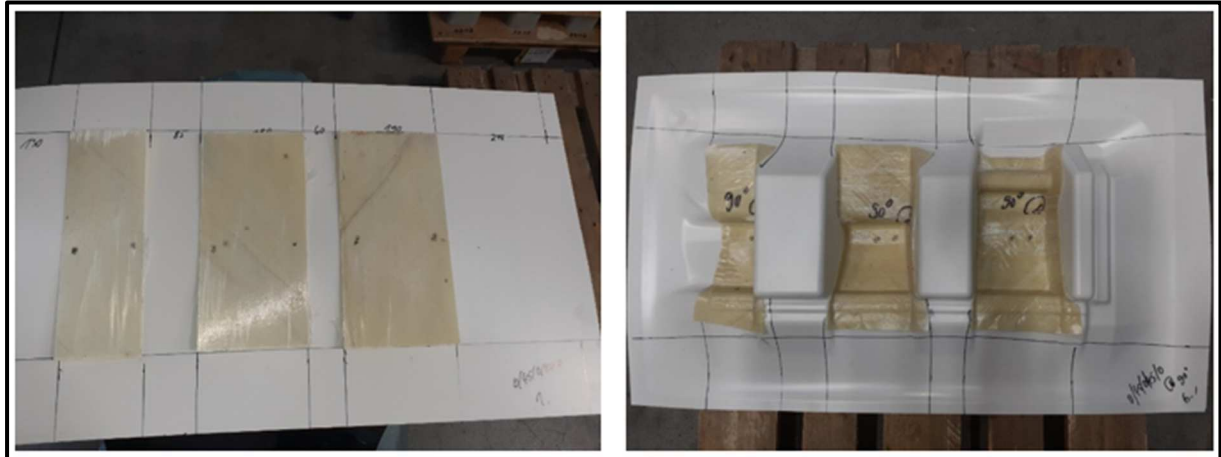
Zuschnitt hybrid ultraschallgeschweißt & thermogeformt / 04.06.24 Lakowa intern.
